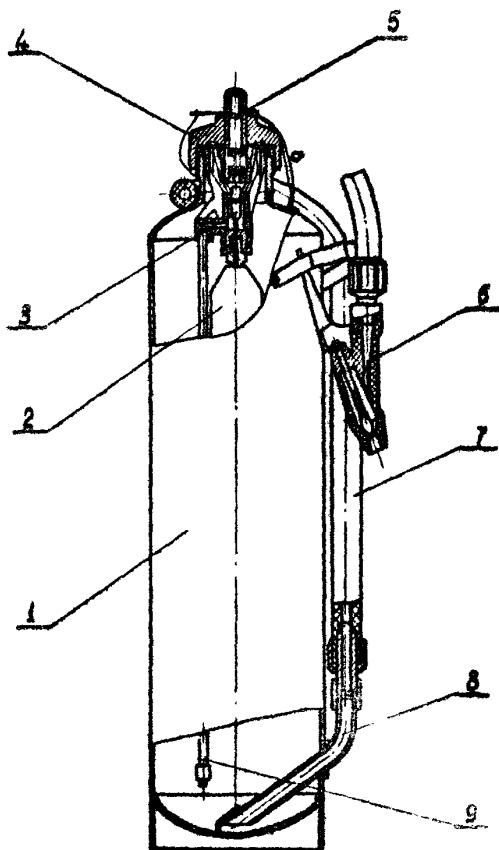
Портативный газопламенный СИ-8У1: 1-металлический корпус; 2-баллон; 3-пробойник; 4-крышка; 5-ударник; 6-наконечник; 7 - ручка; 8-смесительная камера; 9-вспушыватель.
